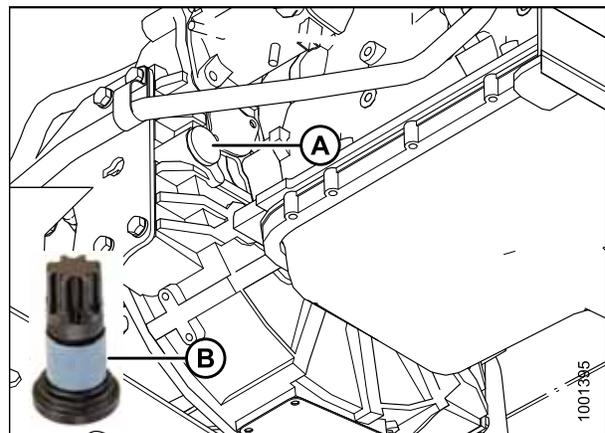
Расположение отверстия для работы инструментом для проворачивания коленвала
